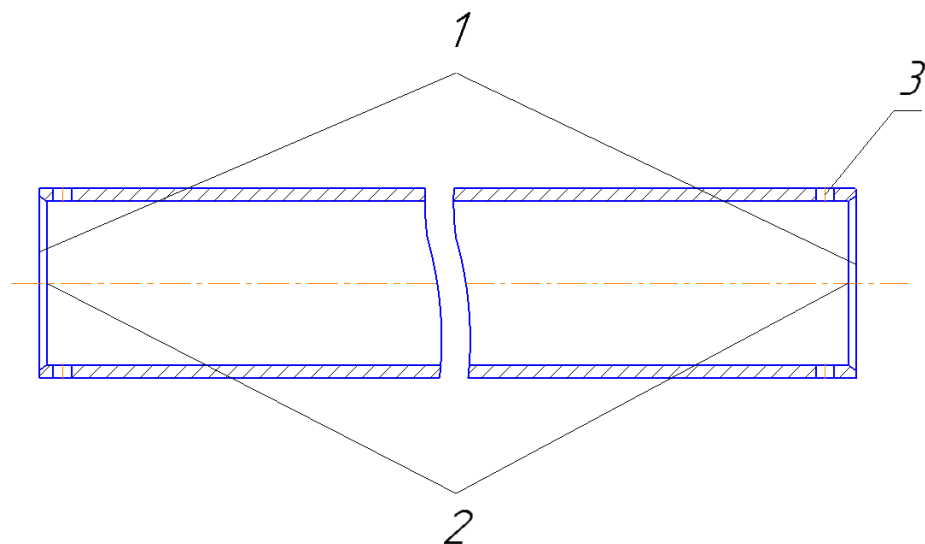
Креслення оброблюваної деталі з необхідними розмірами
